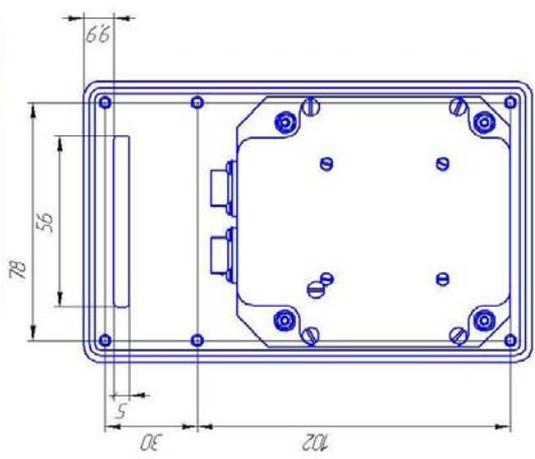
Габаритный чертеж манипулятора шарового оптического МШО-50.х25х
